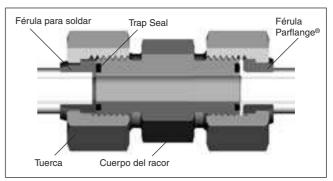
Vista seccionada de la unión O-Lok® con conjuntos soldados (LHS) y embridados
